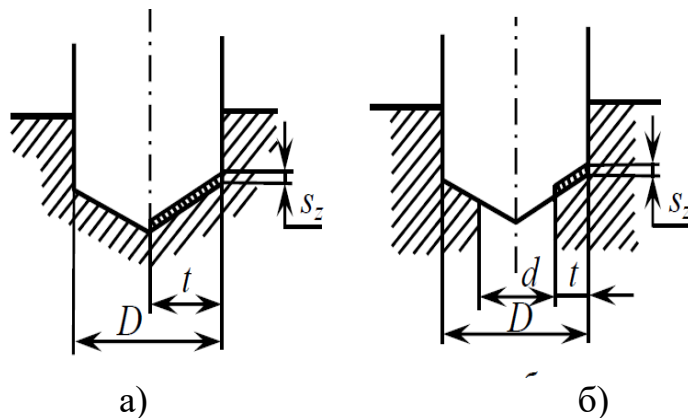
Схема різання: а) – під час свердління; б) – під час розсвердлювання
